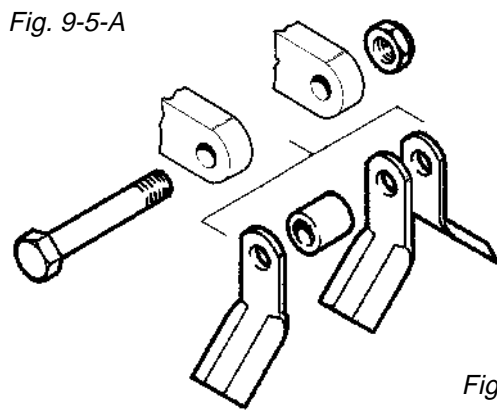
Montaggio coltelli FP e FA - FP and FA knives assembly
